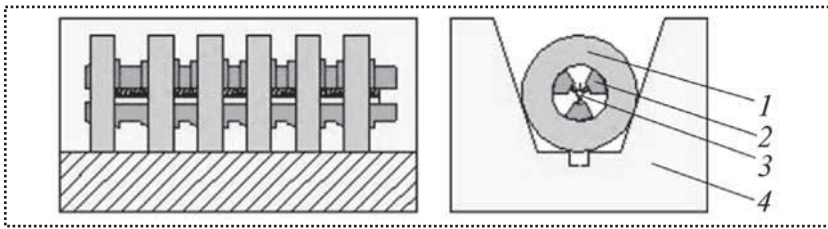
Оправка для проведения диффузионной сварки спирали с керамическими стержнями:
